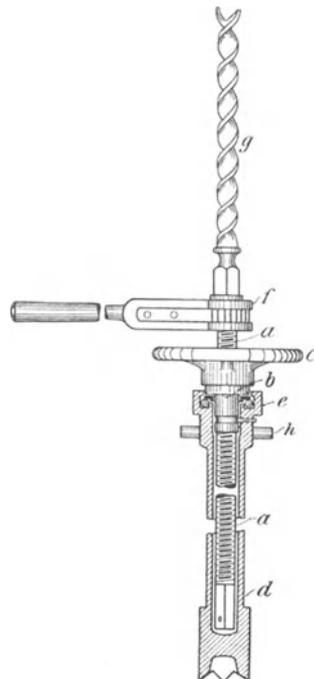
Handbohrmaschine Westfalia mit Handrad.
